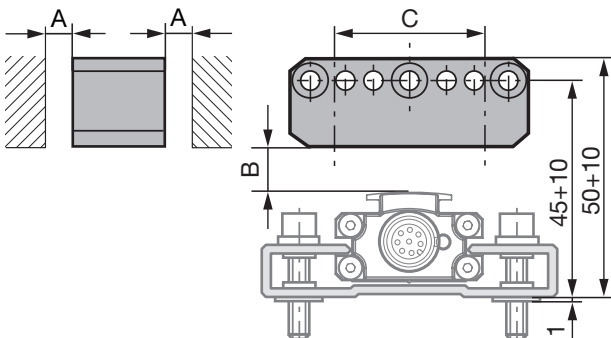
Dimensions et distances pour le capteur de position BTL5-P-5500-2
